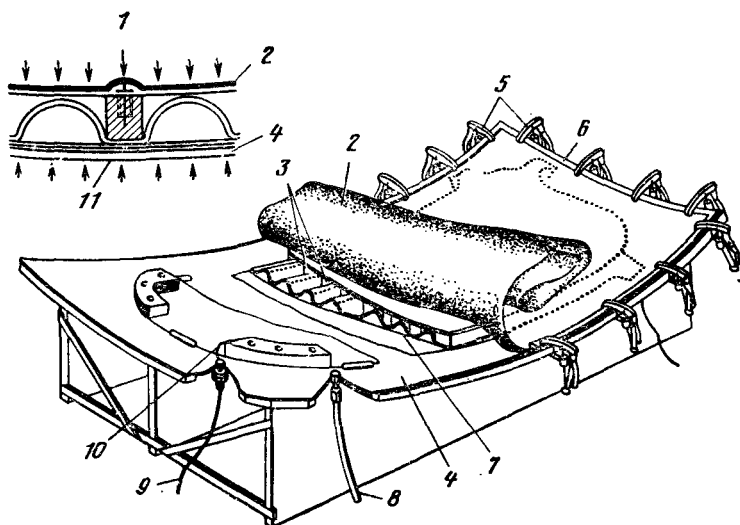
Типовая конструкция приспособления для сборки панели:
